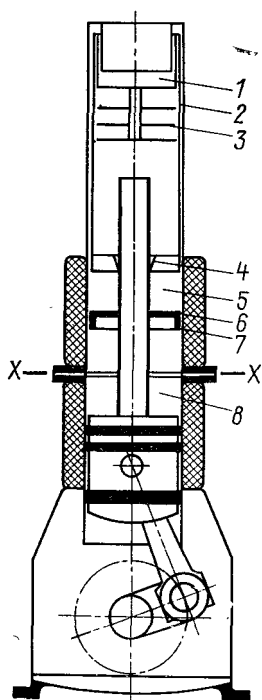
Гибридный двигатель Стирлинга со свободным вытеснителем и кривошипно-шатунным приводом рабочего поршня¹.
